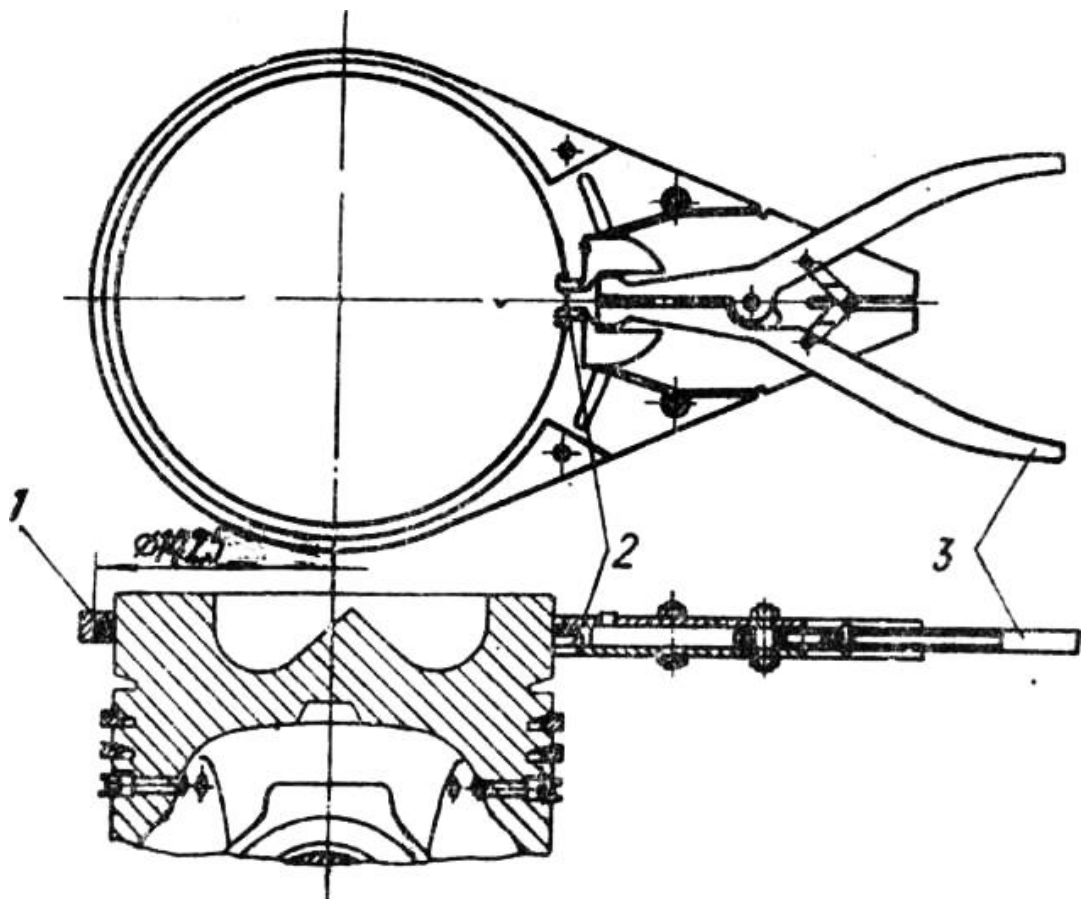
Пристрій для зняття та установки поршневих кілець:
